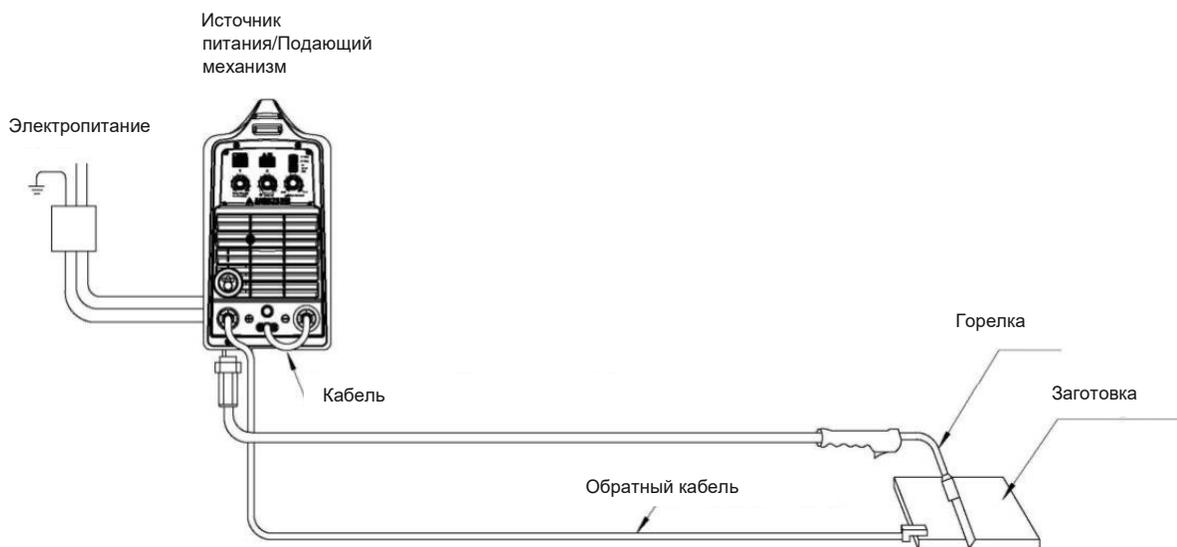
Сварка порошковой проволокой FCAW-S
